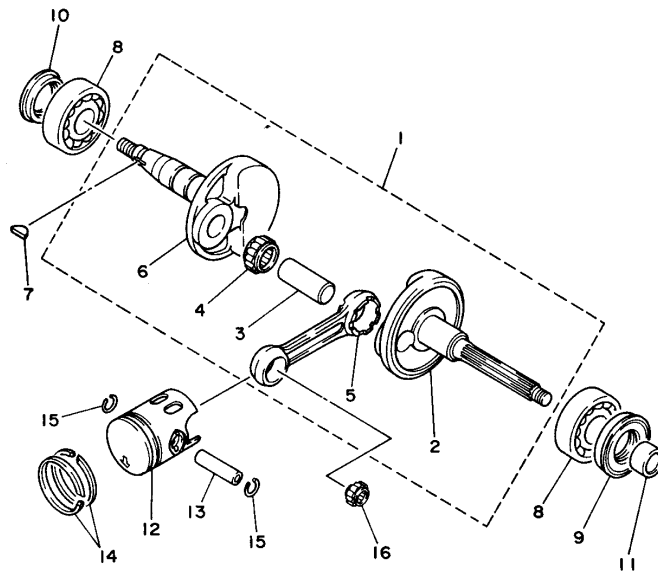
CRANKSHAFT. PISTON CIGUENAL. PISTON
